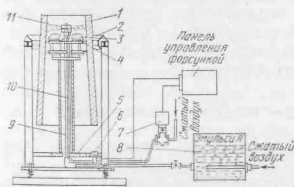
Комбинированная установка для чистки и смазки изложниц
